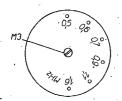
Připevnění a úprava zapinání osvětlovací žárovky
